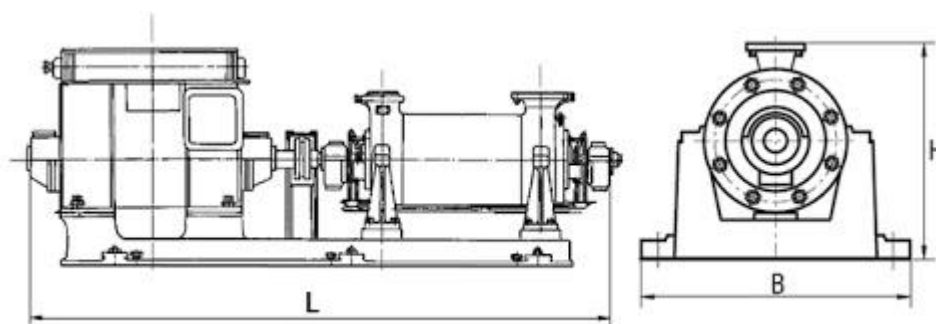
Габаритный чертёж питательного насоса ПЭ-65-53
